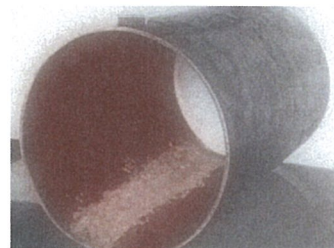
Біметалева обичайка для установок термоядерного синтезу
